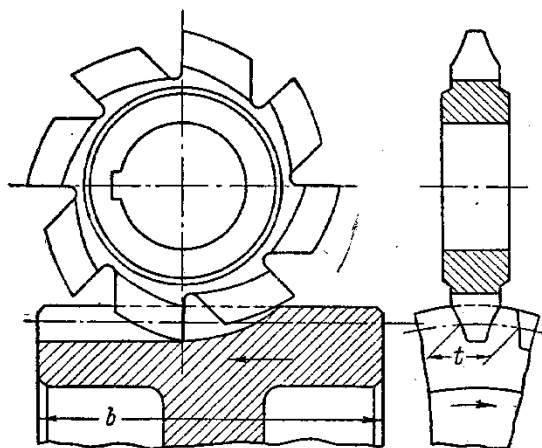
Нарезания зубьев дисковой модульной фрезой с продольным перемещением заготовки
